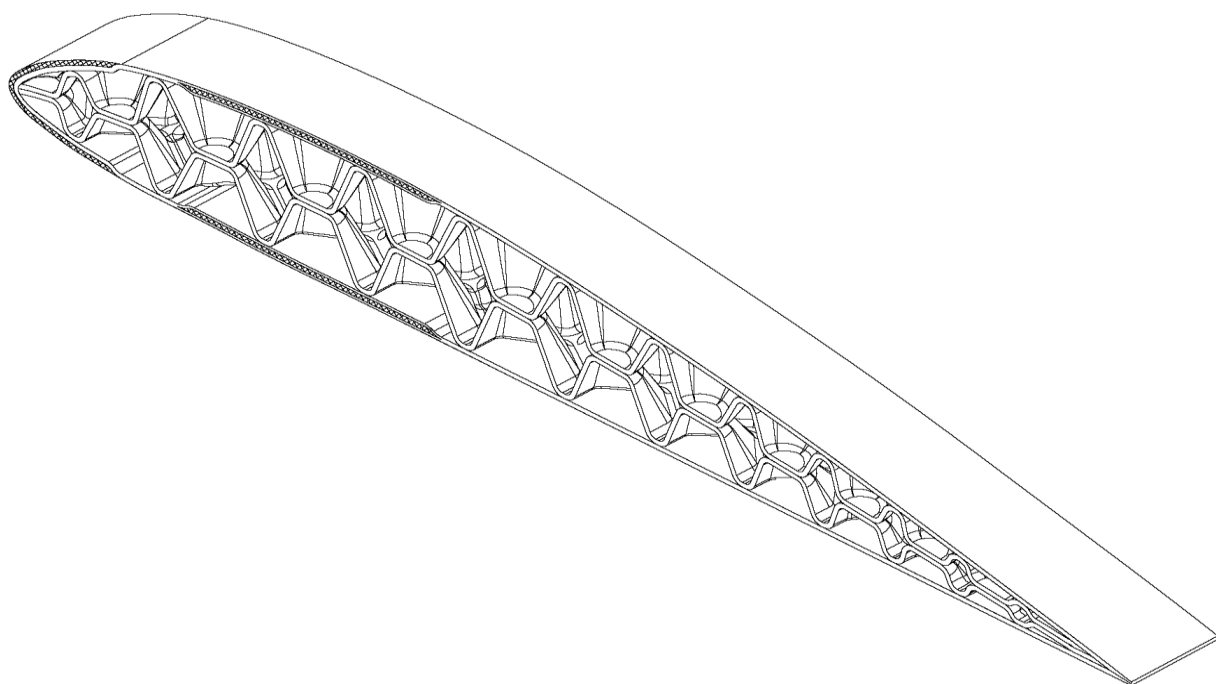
Предлагаемый общий вид конструкции трёхслойного
